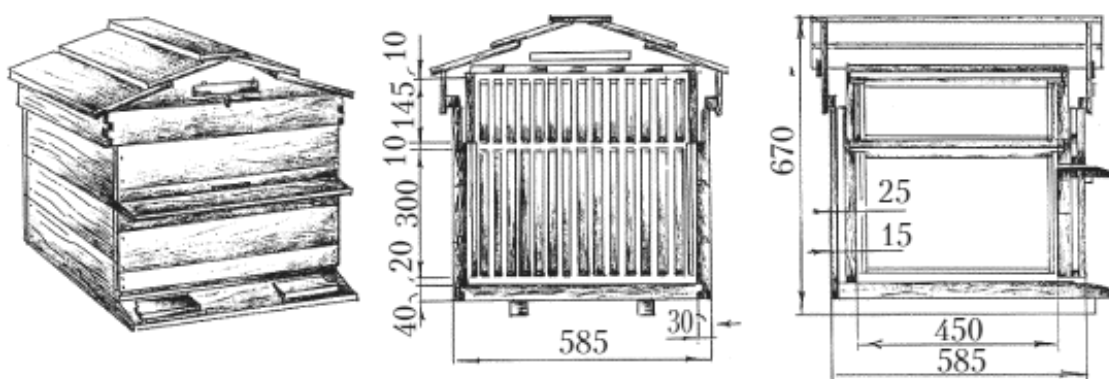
14-рамочный утепленный улей: а – общий вид; б – поперечный и продольный разрез
